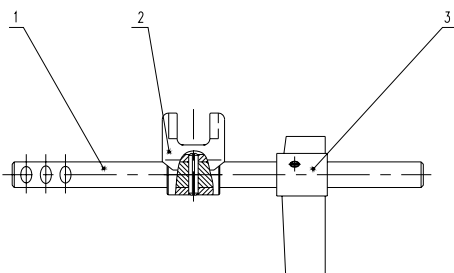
Вал вилки в сборе шестерни третьей и четвертой передачи.
